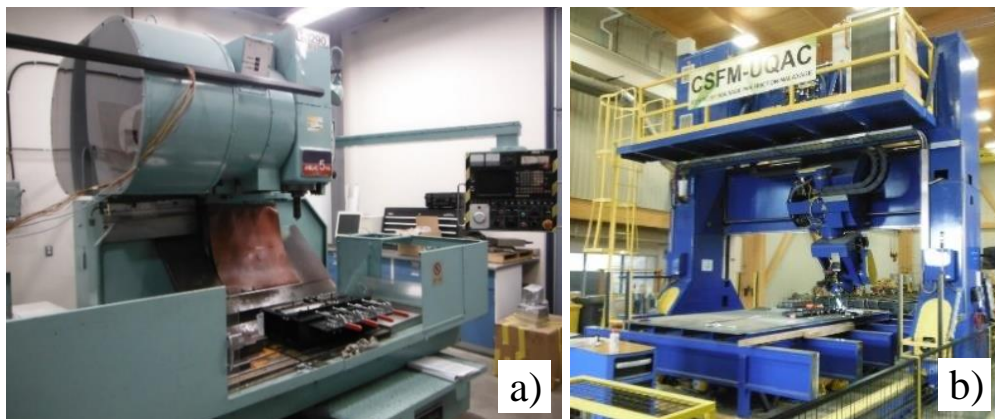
Équipements de soudage par friction malaxage a) Fraiseuse adaptée b) Portique spécialisé
